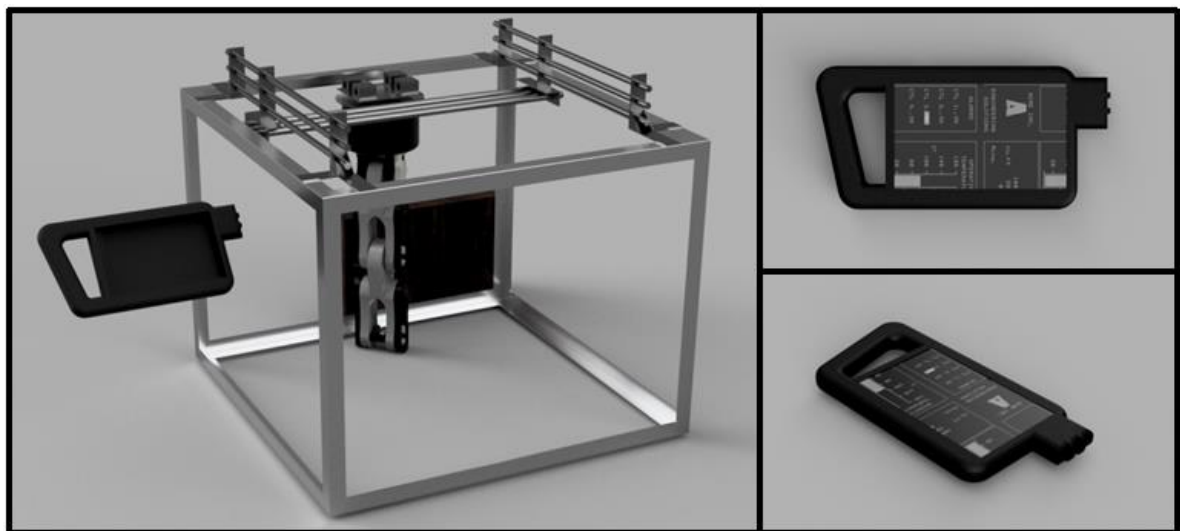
Renderizado de la estructura para la pantalla. Fuente: Autor
